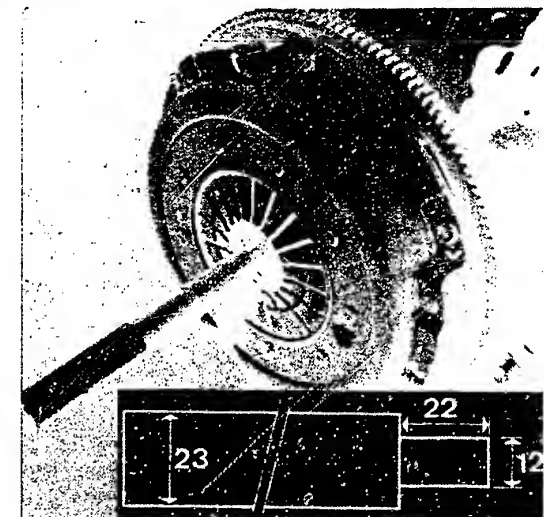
Einbau der Kupplung mit dem Zentrierdorn.
